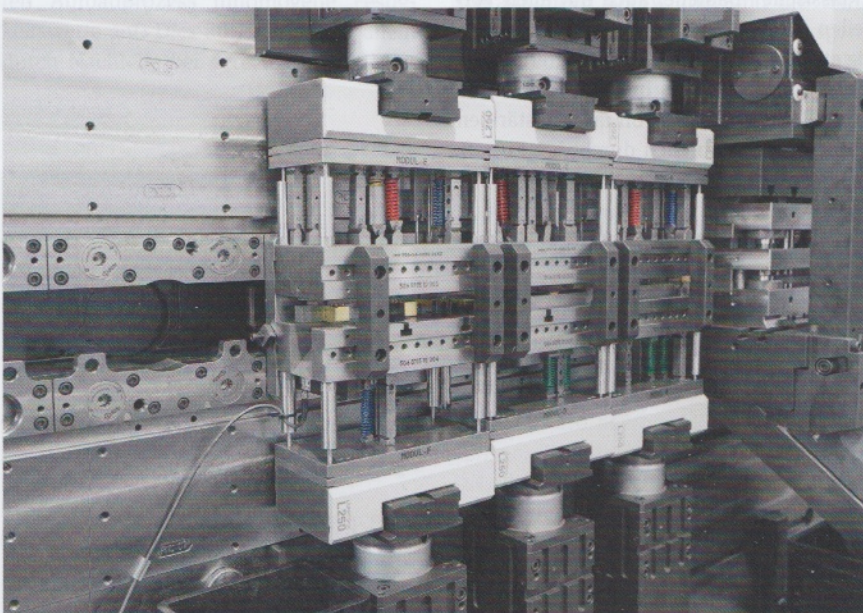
> Bei den Linearmaschinen dauert ein Werkzeugwechsel aufgrund der Modulbauweise und der Nullpunktspanntechnik nur rund eine Stunde (© Andreas Maier GmbH & Co. KG)
